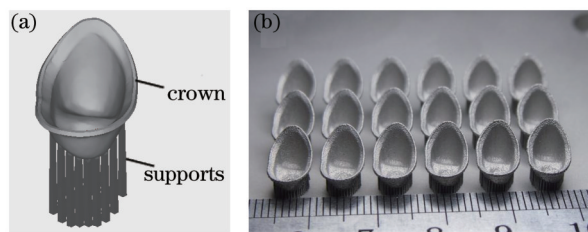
个性化牙冠成型。(a) CAD 模型; (b) SLM 牙冠
